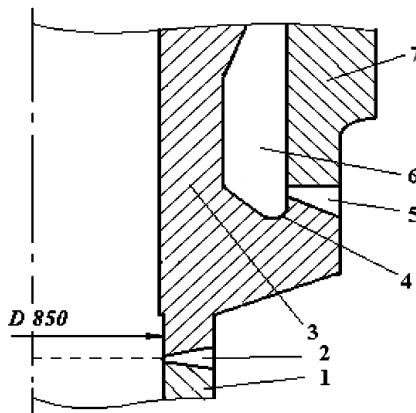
Фрагмент конструкции узла приварки горячего коллектора к корпусу ПГ: 1 – главный циркуляционный трубопровод; 2 – сварной шов; 3 – коллектор; 4 – галтель; 5 – сварной шов № 111; 6 – карман; 7 – патрубок.
